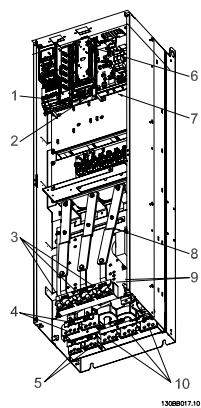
Compact IP 00 (Шасси), размер корпуса D3
